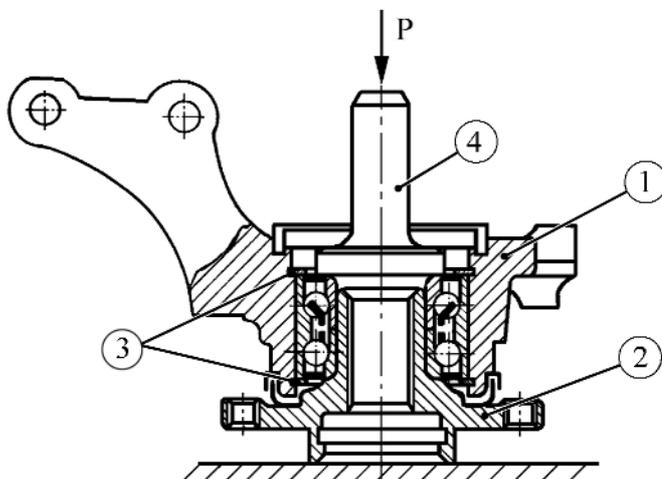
Напрессовка подшипника на ступицу переднего колеса:
